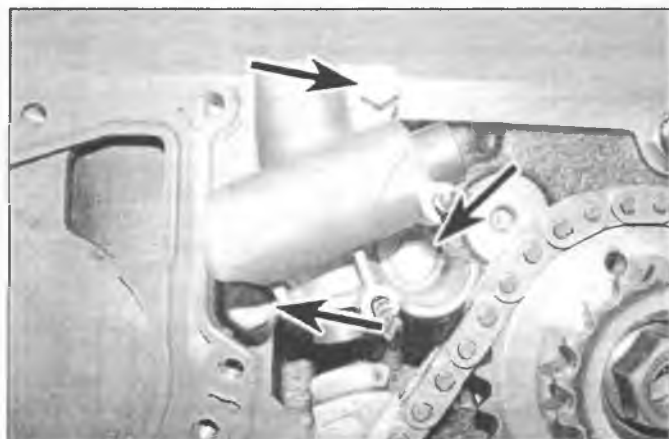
Выверните три болта (отмечены стрелками) и снимите натяжитель с блока цилиндров
